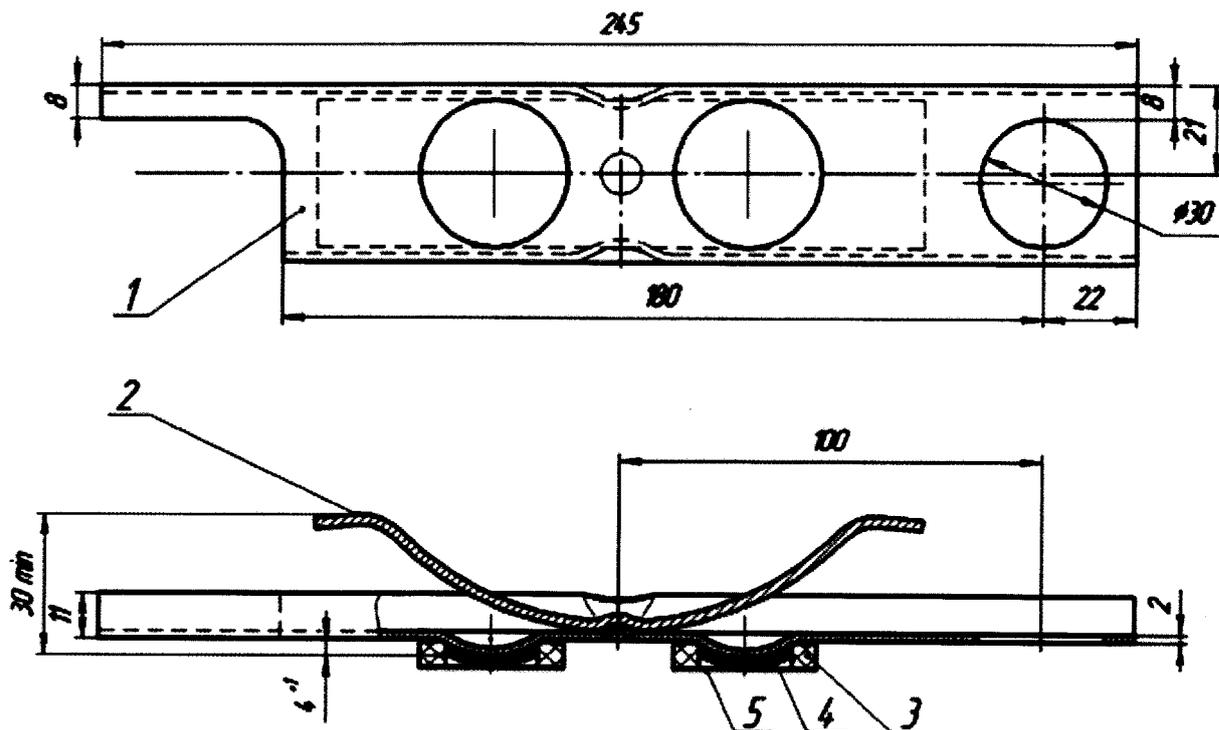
Схема монтажа рельсового стыкового пружинного соединителя.
